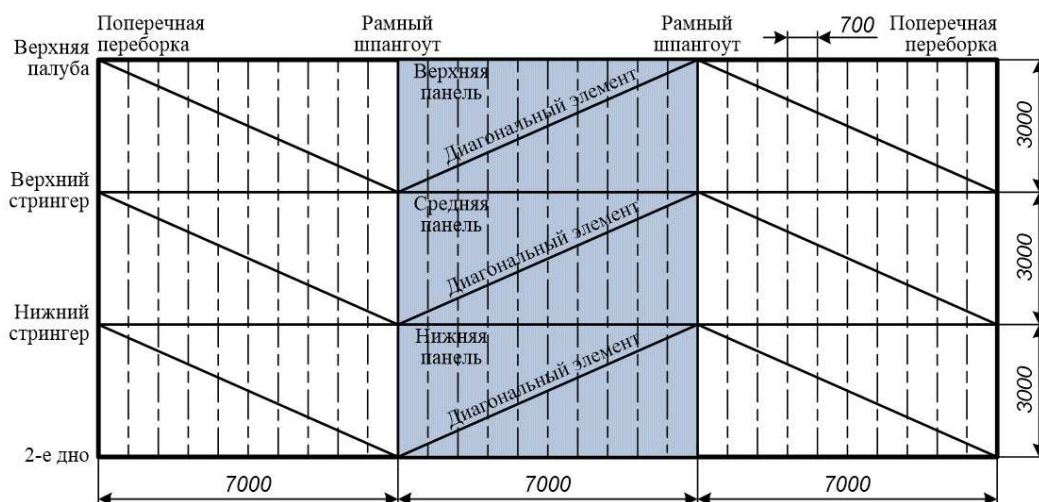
Расчетная схема набора бортового перекрытия с диагональными элементами
